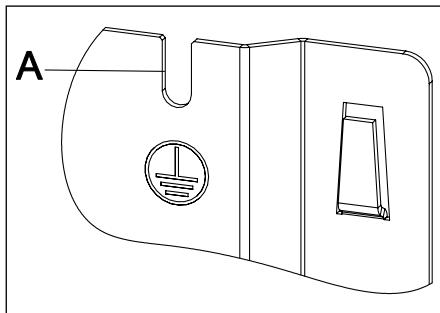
Collegamento equipotenziale di protezione / Messa a terra
